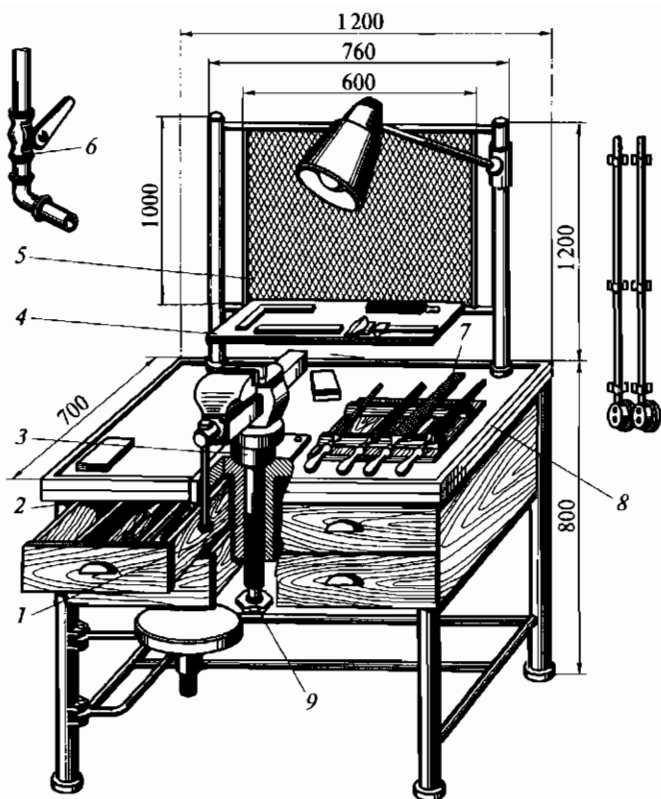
Расположение инструментов и оборудования на слесарном одноместном верстаке с поворотными тисками, регулируемым по высоте: 1 — винт; 2 — каркас; 3 — гайка; 4 — полка; 5 — экран; 6 — труба подвода сжатого воздуха; 7 — планшет для инструмента; 8 — рамка; 9 — маховичок
